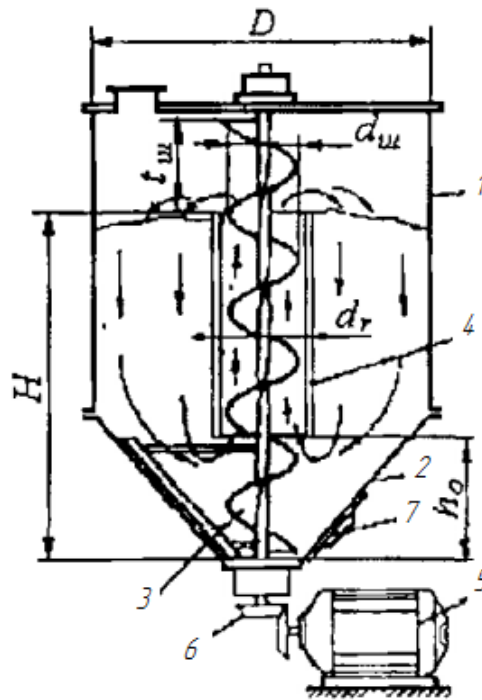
Схема лабораторного циркуляційного змішувача зміненої конструкції:
